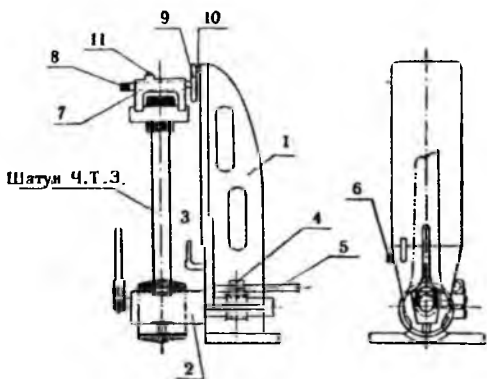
Прибор для проверки и правки шатунов в рабочем положении при проверке изгиба шатуна:
